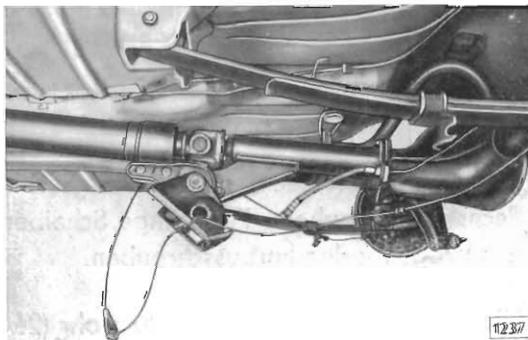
Hinterachse mit Gelenk und Stützrohr mit Gelenkwelle bis zum Freihängen abgelassen
